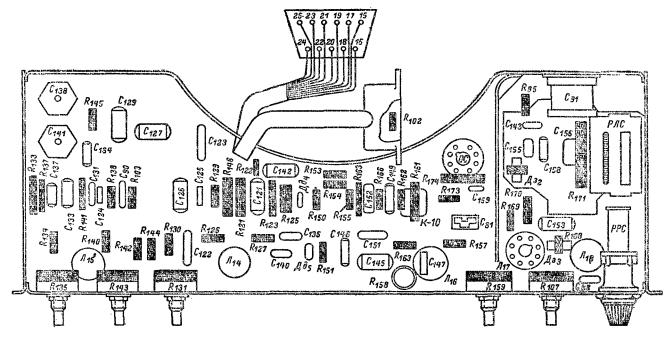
Расположение деталей на шасси блока развертки телевизора «Рубин-102В» (вид со стороны монтажа).
